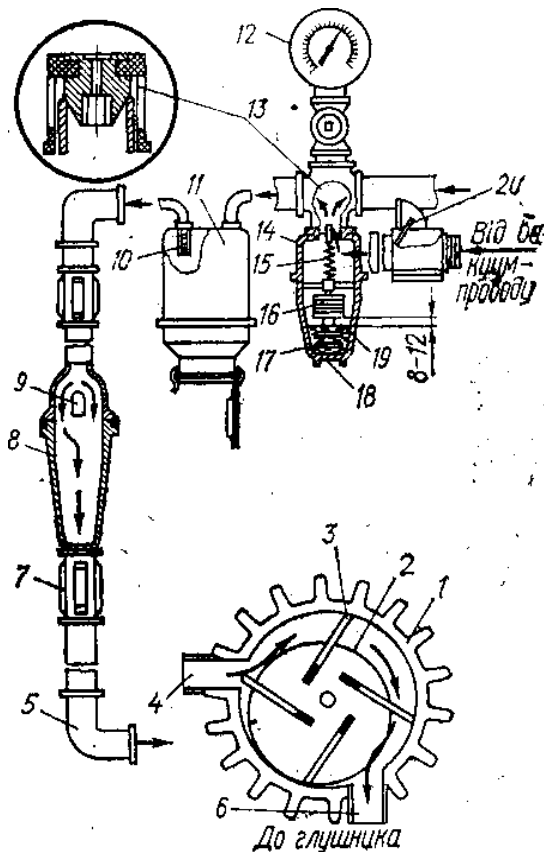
Схема вакуумної установки УВУ-60/45:
